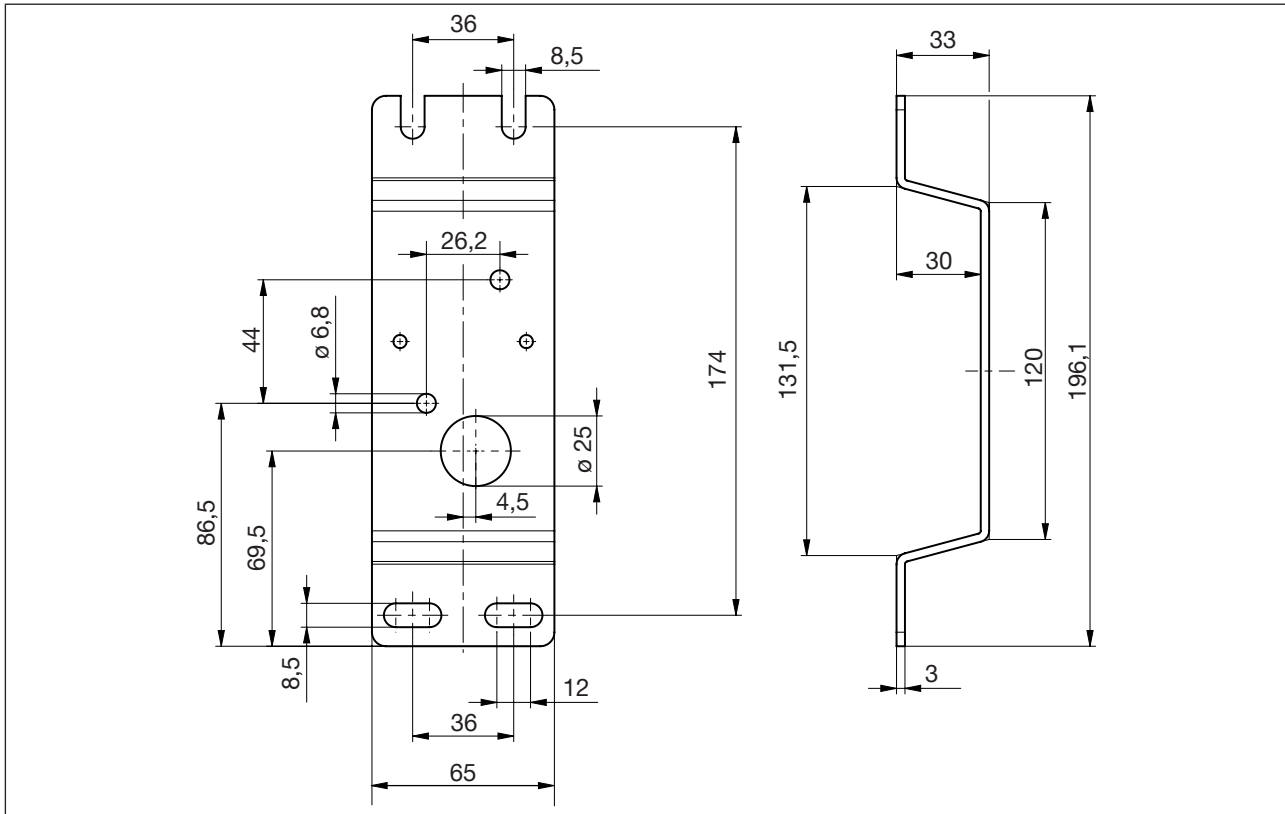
Dimensions de l'équerre de fixation préinstallée
